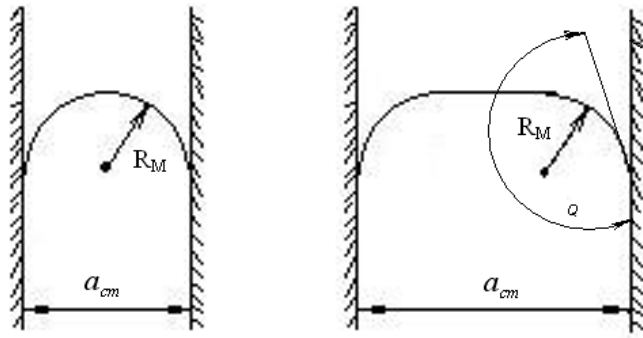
Утворення меніску в порожнині ливарної форми
